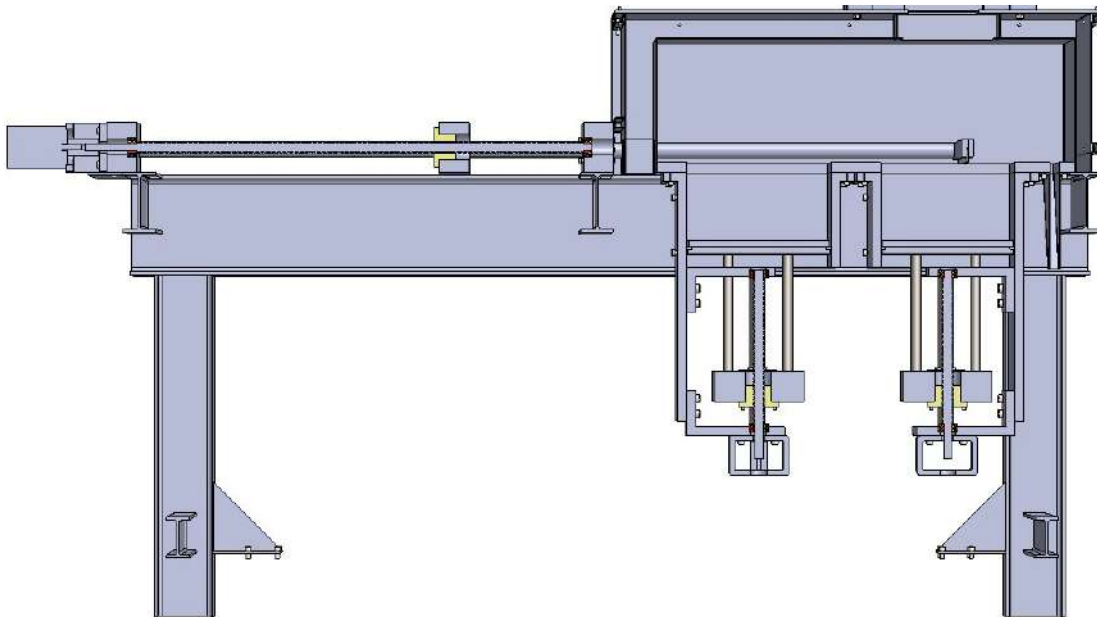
CAD da máquina no estado inicial vista em corte.
